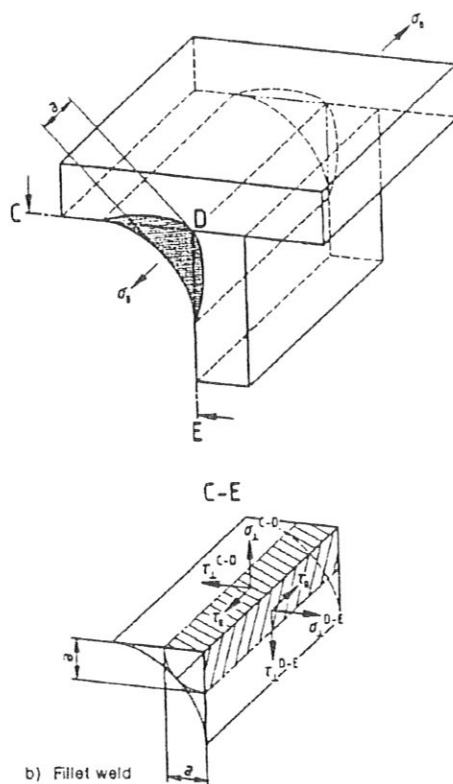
assemblage soudée (selon DIN 18 800-1)
